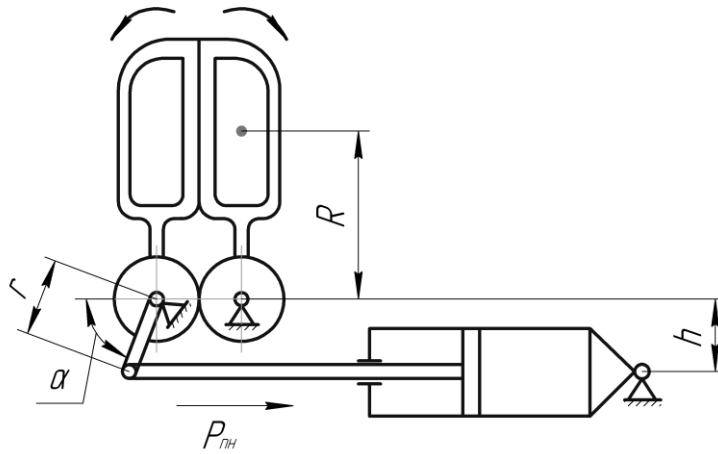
Розрахункова схема для підбору пневмоциліндра пристрою захоплення та утримання плівки
